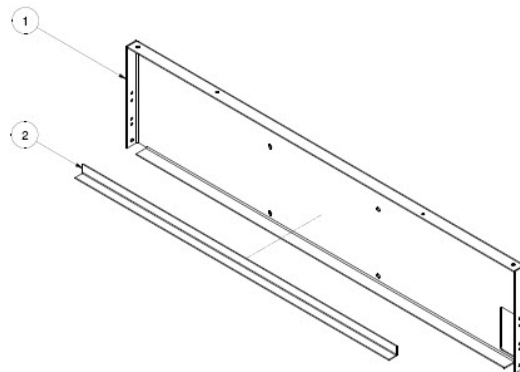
(Vista explosiva del ensamble. Los componentes uno y dos son la charola y ángulo refuerzo respectivamente. La unión entre ellos es por medio de soldadura MIG).
